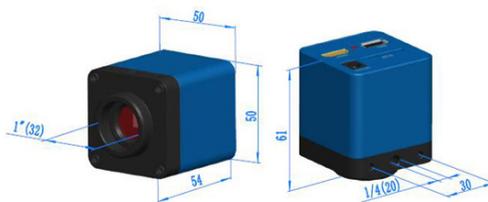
00 Dimensions du produit (mm) de la MikroCam MINI Full HD HDMI
